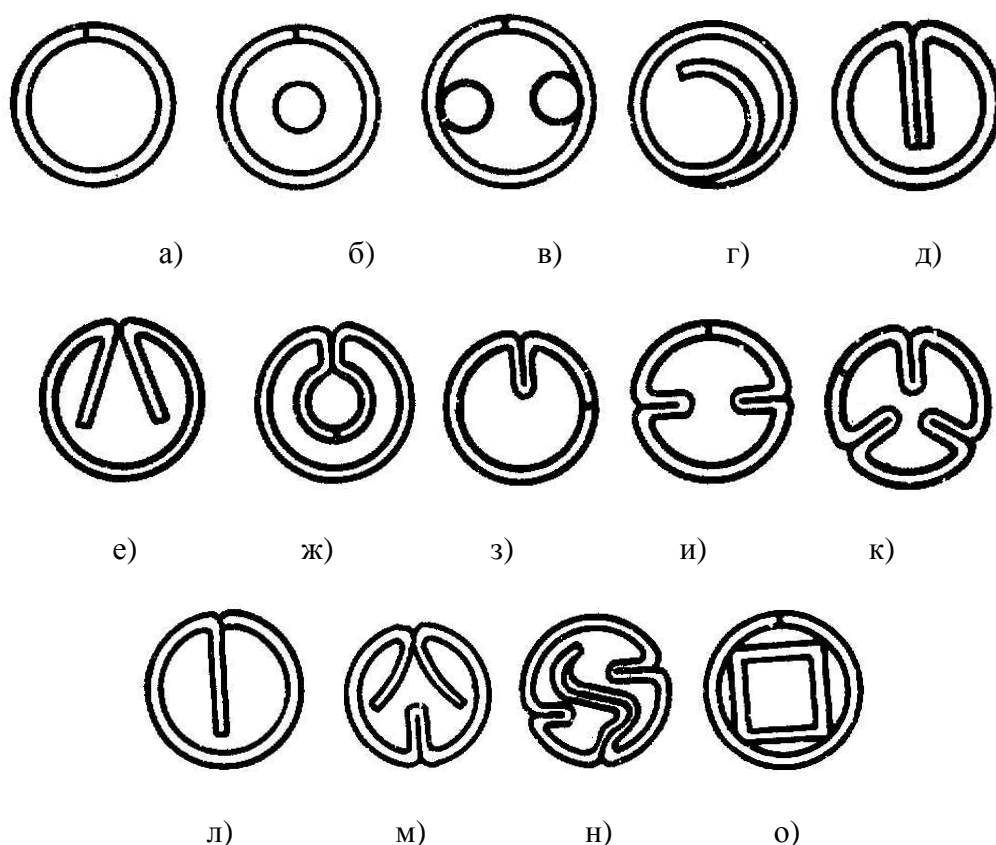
Поперечное сечение порошковой проволоки разных конструкций
